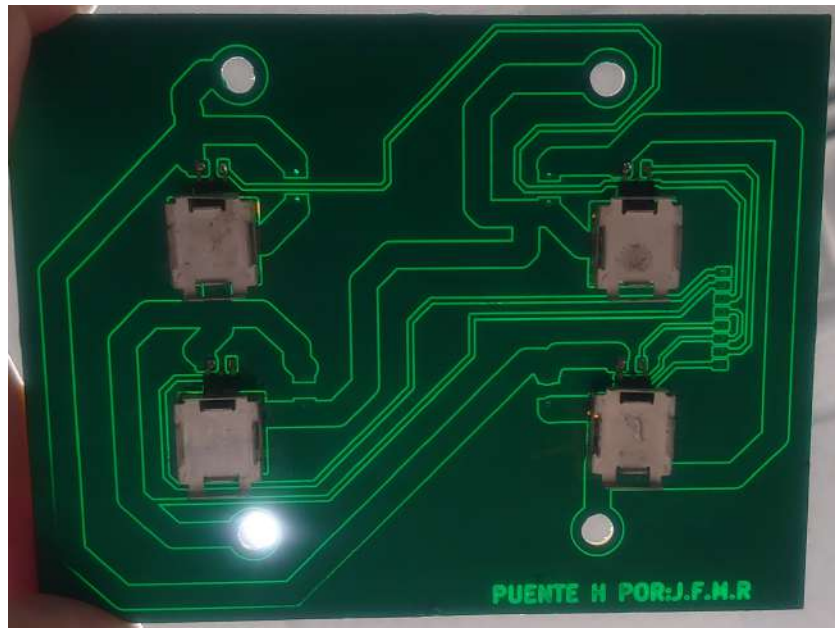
Puente H con máscara anti soldadura.
